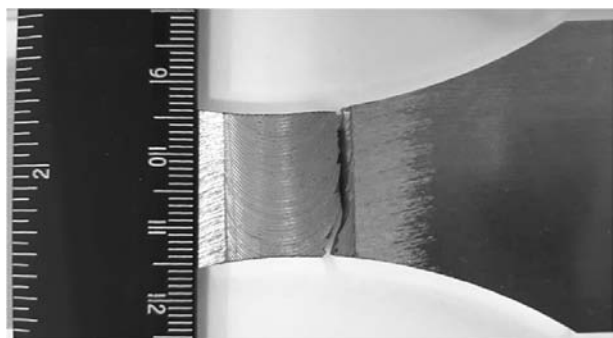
Разрушение образцов сварных соединений сплава ВАЛ8, выполненных СТП
